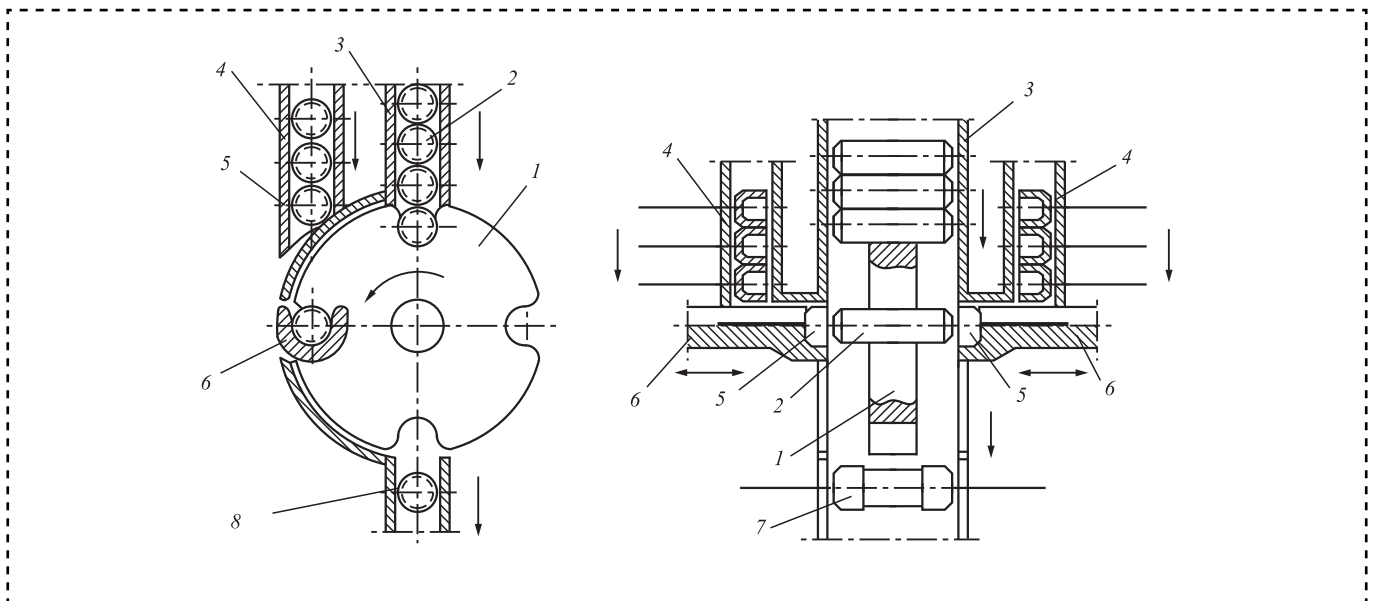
Сборочная установка 2-го типа для напрессовки на основание резистора колпачков с контактными выводами:
